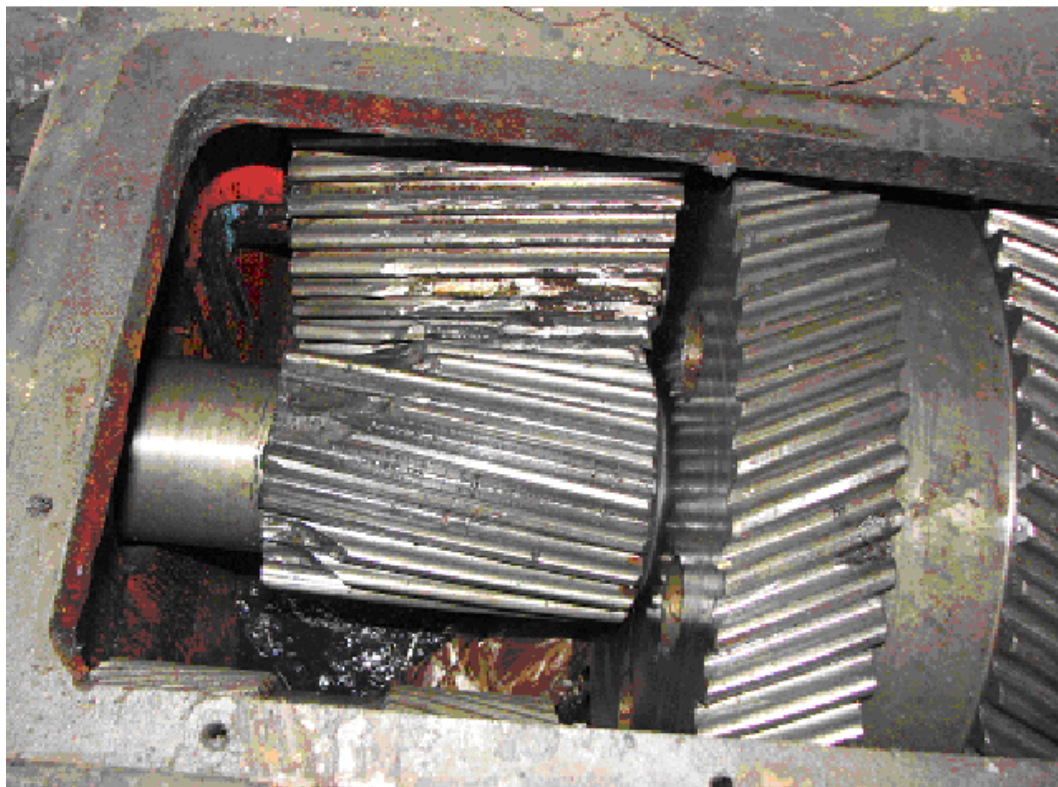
Руйнування зубчатих пар внаслідок поломки привідного вала
